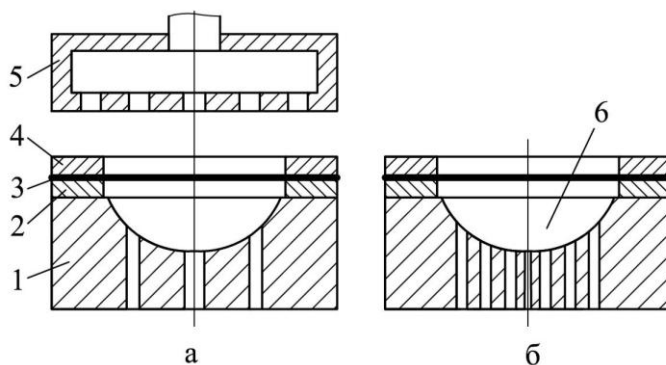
Схема пневматичного і вакуумного формування
